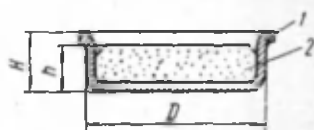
Крышка ртутно-цинкового элемента с запрессованным цинковым порошком:
